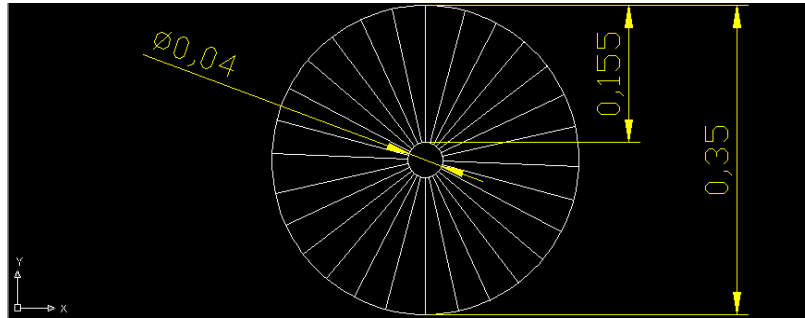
Dimensiones del rotor, en unidades del sistema internacional SI (m).
